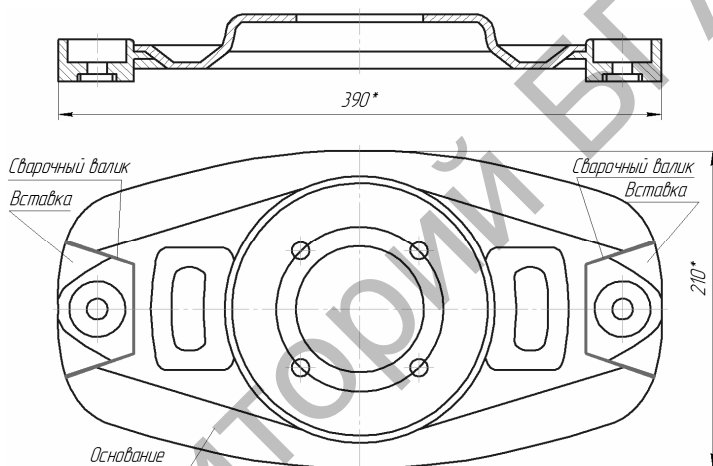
Эскиз диска ротора режущего аппарата косилок
